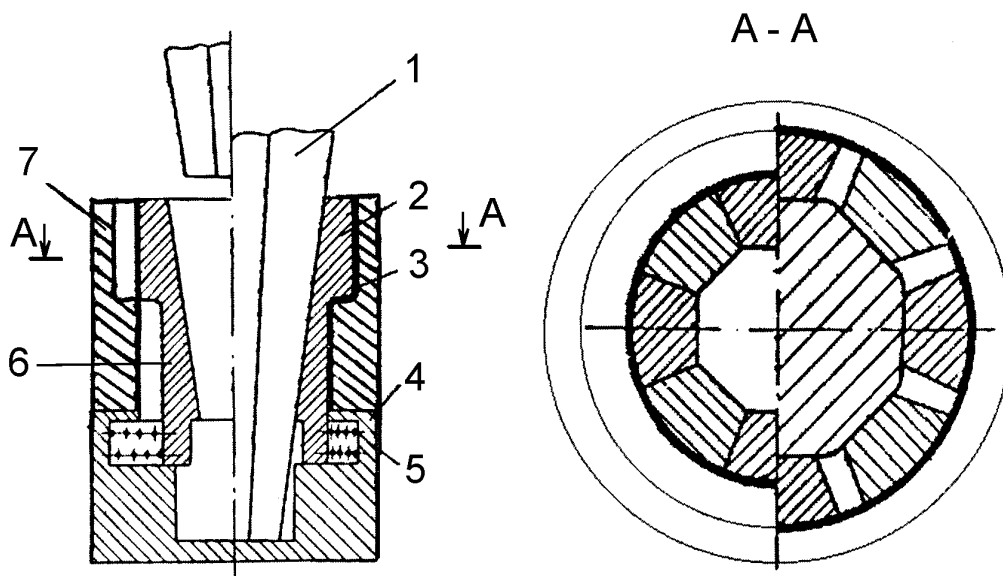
Формоутворення деталей роздаванням розтискним пуансоном: 1 – клин; 2 – розтискний пуансон; 3 – деталь; 4 – плита; 5 – пружина; 6 – заготовка; 7 – матриця
